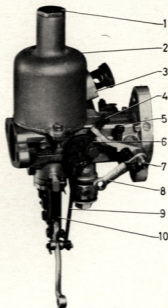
Carburateur arrière vu du côté des organes de réglage.
